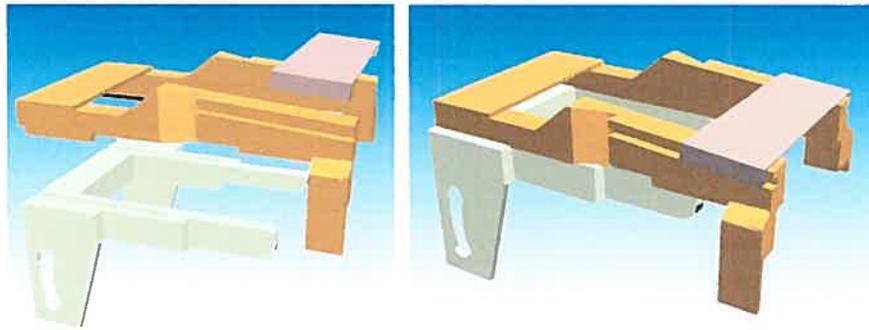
Dessin de l'explosive et l'assemblage du sixième modèle 3D.¹⁶⁷
